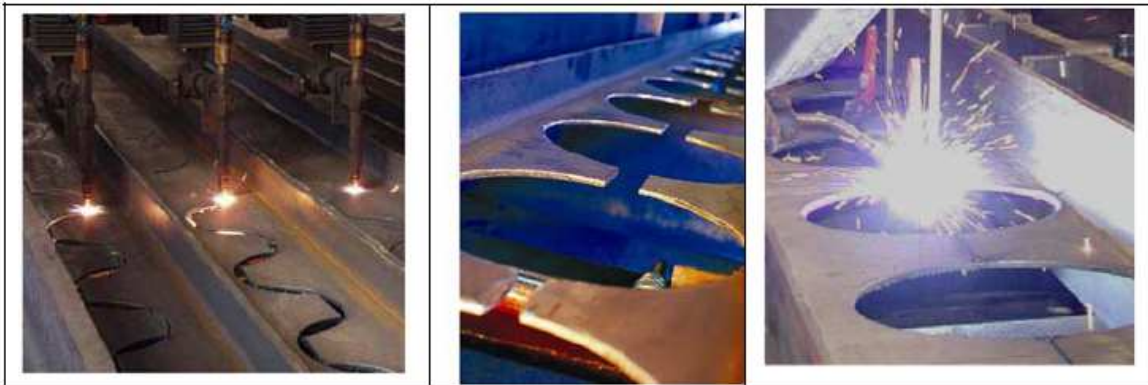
Oxycoupage du profilé de base, séparation et soudage des deux parties [1]
